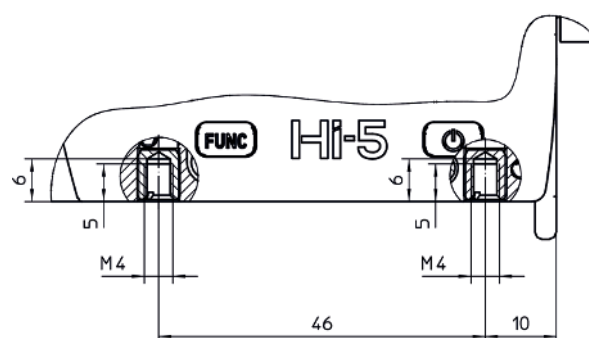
Hi-5 : dettaglio vista frontale Y
